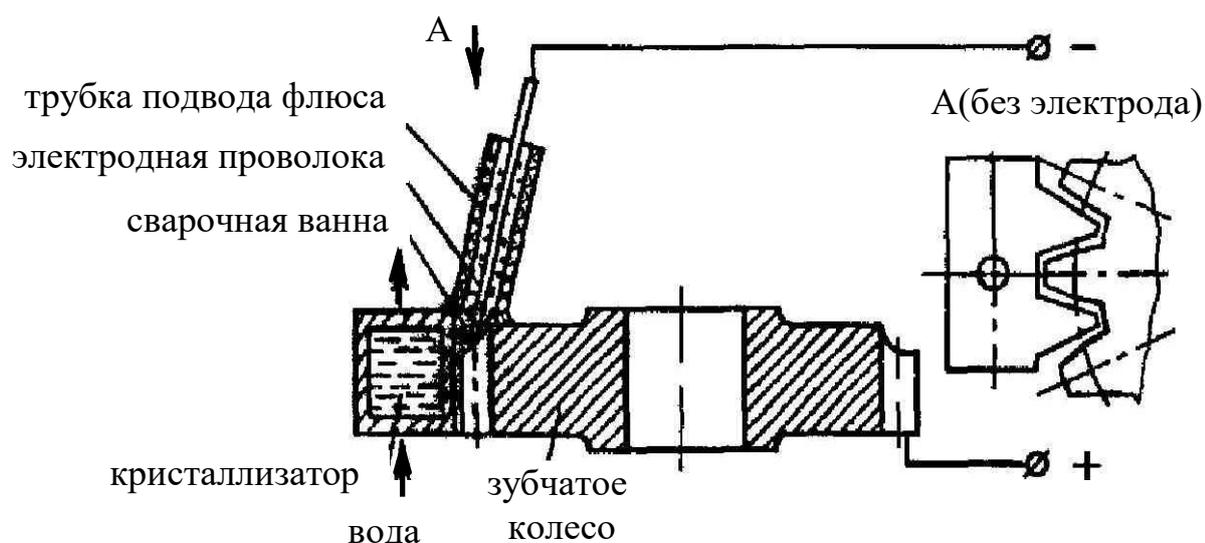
Наплавка торцов зубьев в кристаллизаторе
